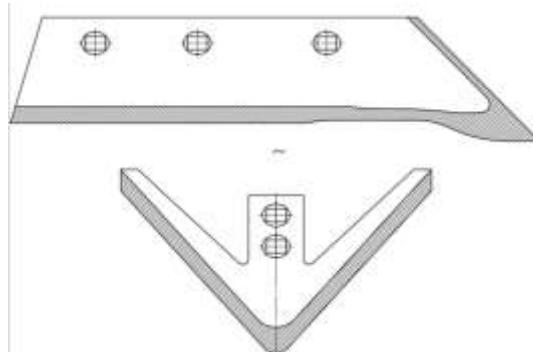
Изменение профиля при изнашивании: а — лемеха плуга; б — лапы культиватора
